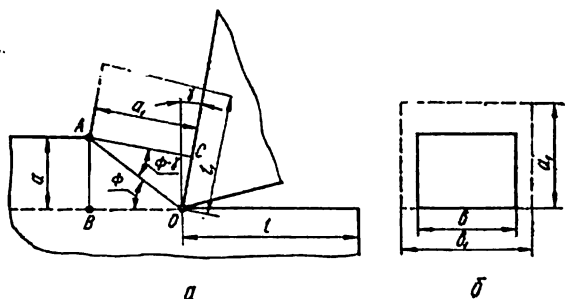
Схема определения усадки стружки в продольном (а) и поперечном (б) сечениях.
